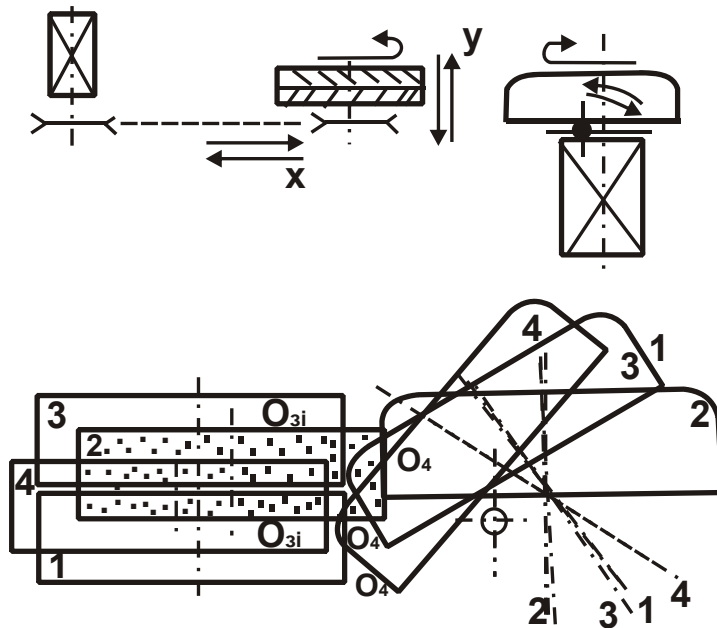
Схема руху інструмента та деталі під час обробки зовнішньої поверхні (а) і положення інструмента та деталі в процесі обробки (один цикл) (б)
